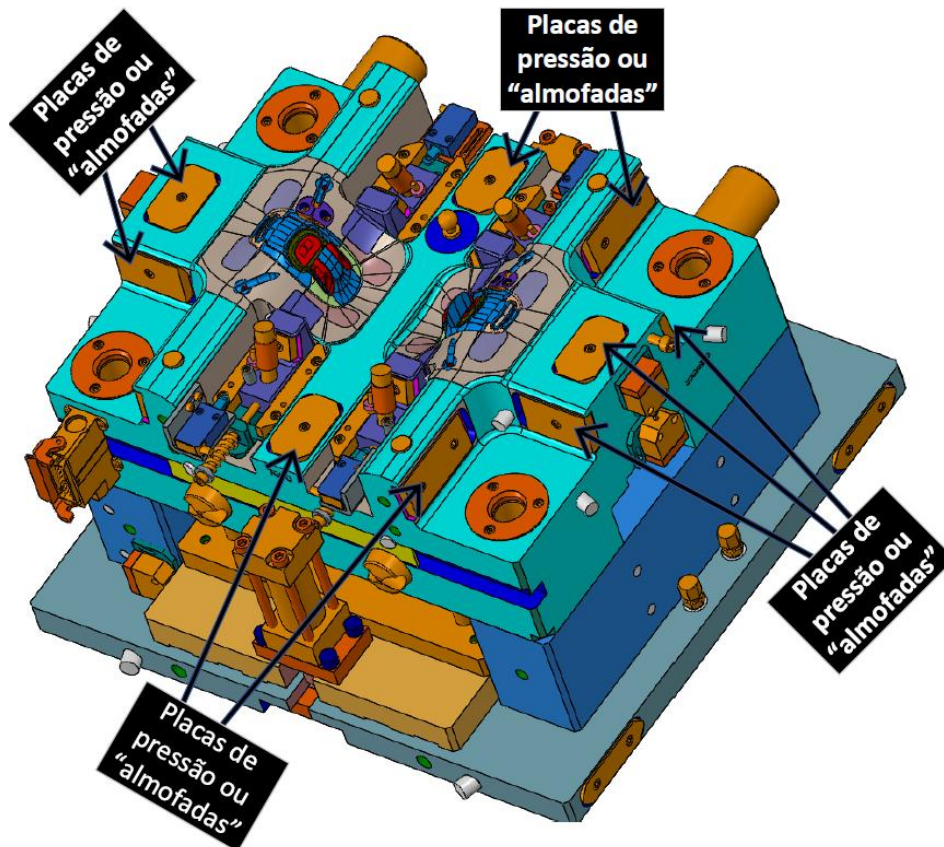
Vista isométrica para as placas de pressão ou "almofadas" do molde (Lado 1)
